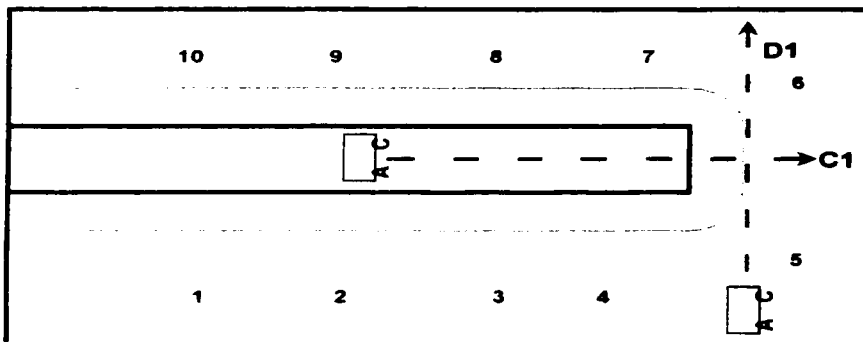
Barrido a través de la unión (grieta al final del pié de soldadura).
